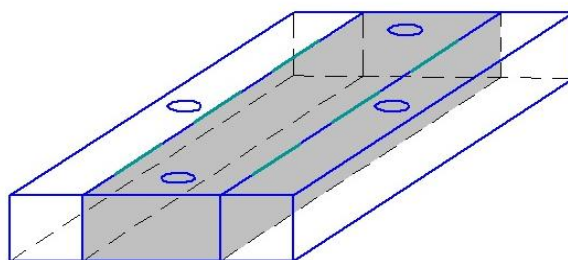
Заготовка контрольного образца с просверленными отверстиями
